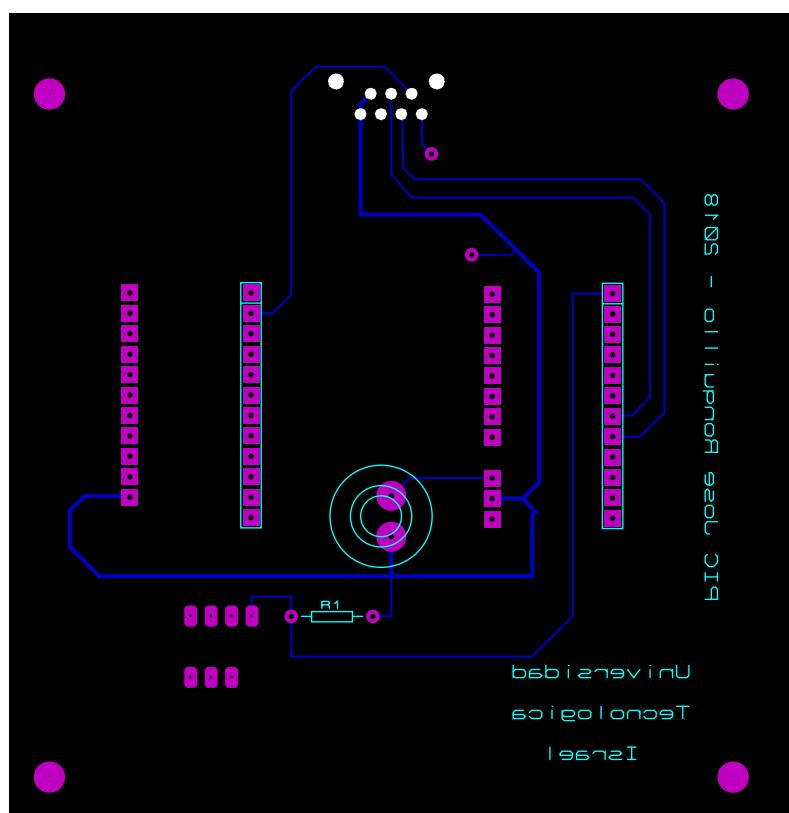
13. Placa de circuito impreso vista desde el lado de los componentes
